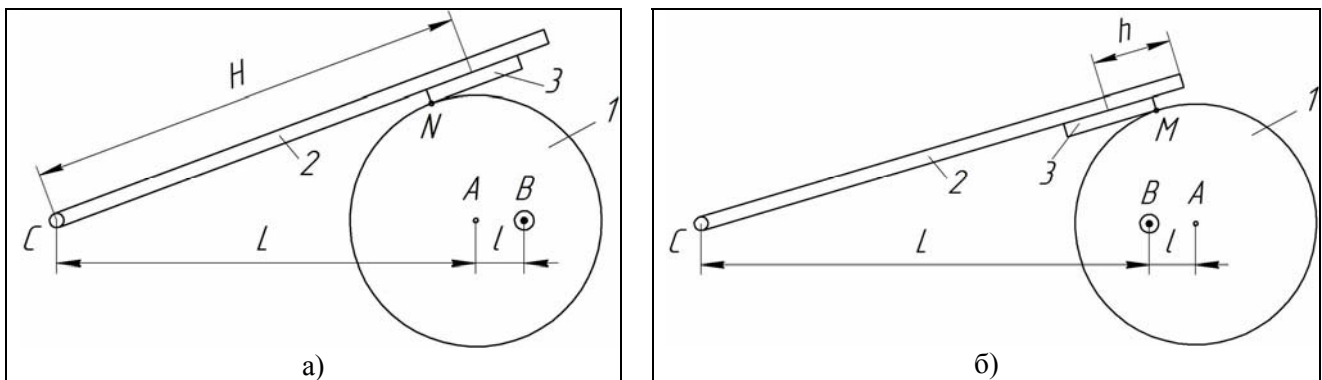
Схема положення оброблюваної деталі на різних етапах обертання спеціального робочого інструменту: а) - саме ближнє положення поверхні оброблюваної деталі до осі повороту тримача; б) - саме дальнє положення поверхні оброблюваної деталі до осі повороту тримача
